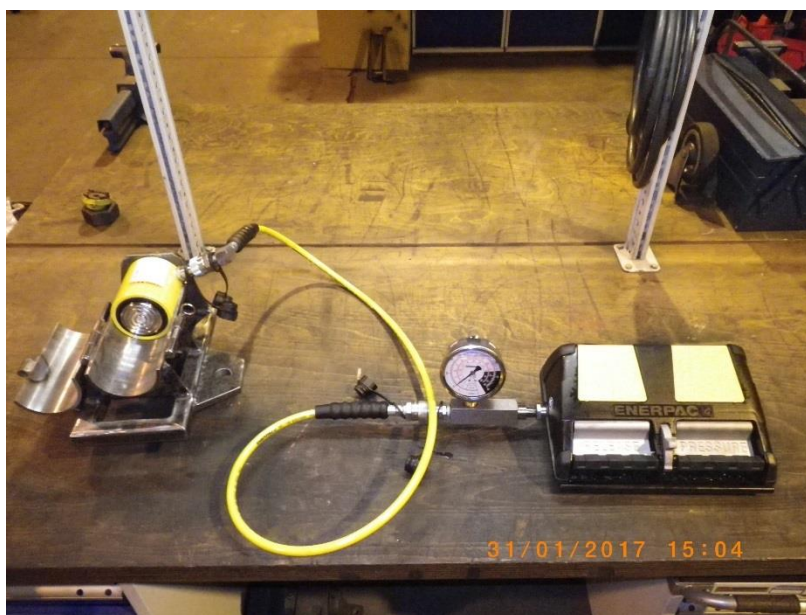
Vorrichtung inklusive Hydraulikzylinder und lufthydraulischer Pumpe [4]
